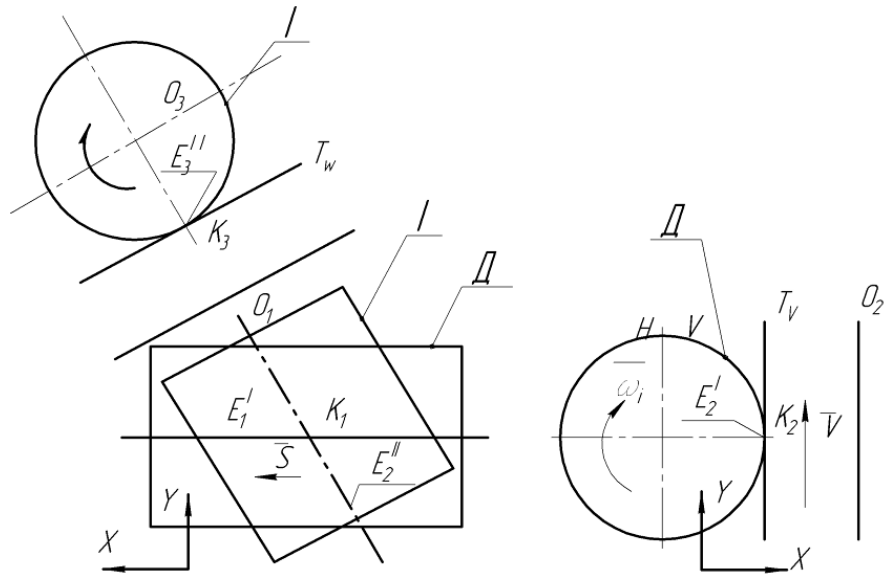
Визначення вихідної інструментальної поверхні, утвореної за другим способом для круглої циліндричної поверхні
